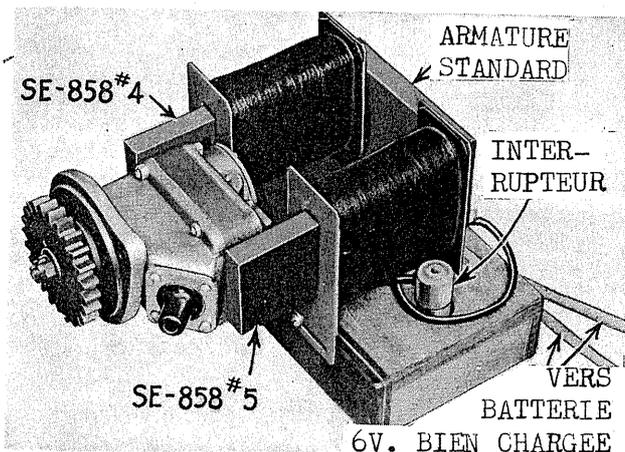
MAGNETO TYPE "H" EN POSITION POUR ETRE RECHARGÉE PAR LE MAGNETISEUR A BOBINES SE-858.
